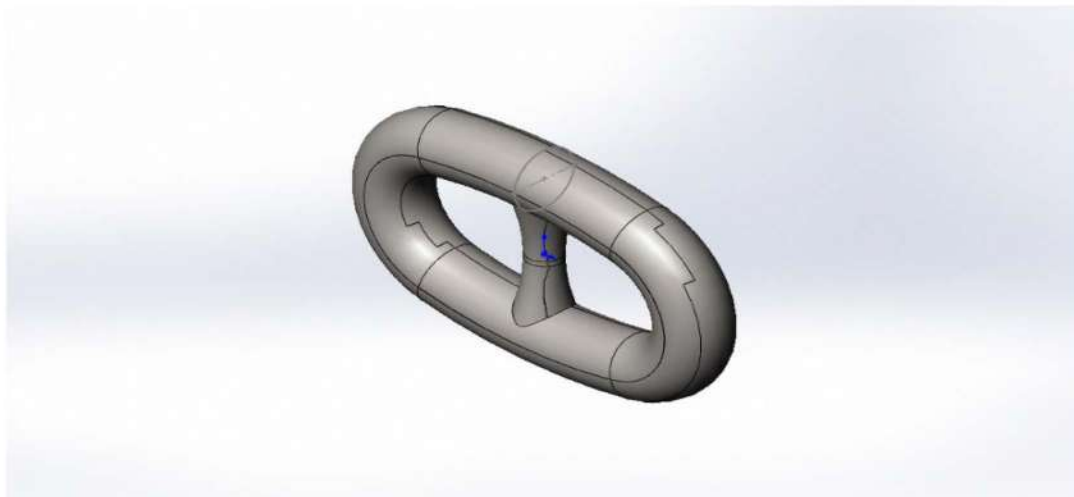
Загальний вигляд ланки якірного ланцюгу з контрфорсом
